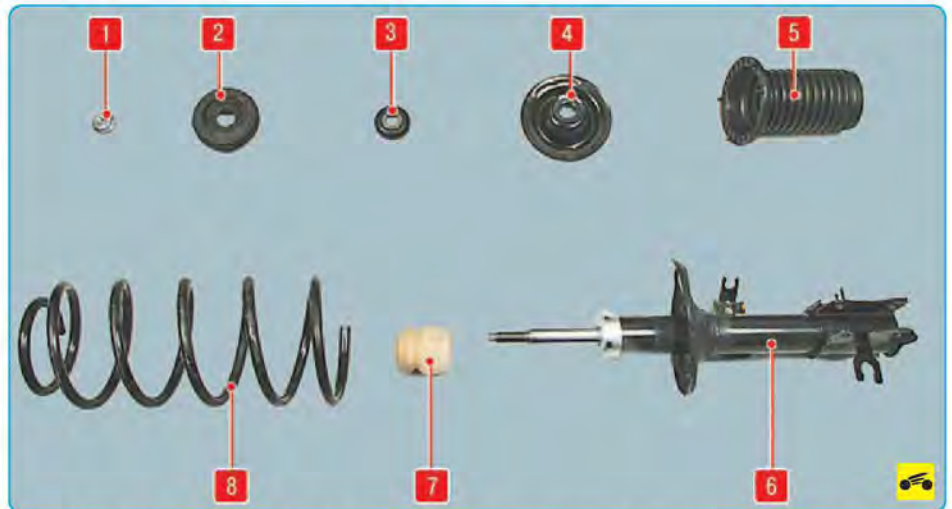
Детали амортизаторной стойки: 1 – гайка штока амортизатора; 2 – верхняя опора стойки; 3 – опорный подшипник; 4 – верхняя опорная чашка; 5 – защитный чехол; 6 – амортизатор; 7 – буфер сжатия; 8 – пружина
